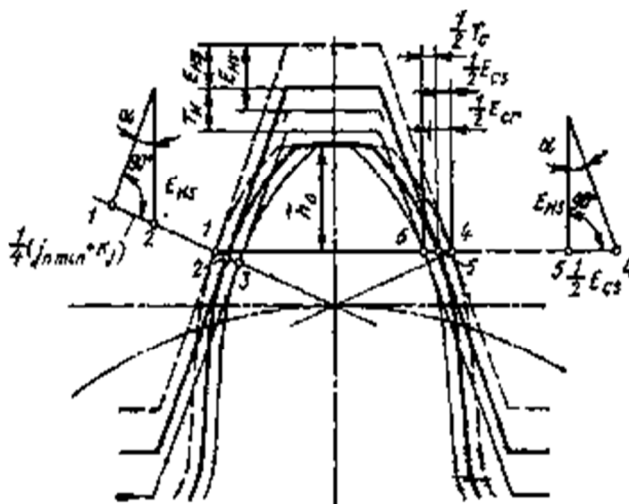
Схема зменшення товщини зубів колеса
